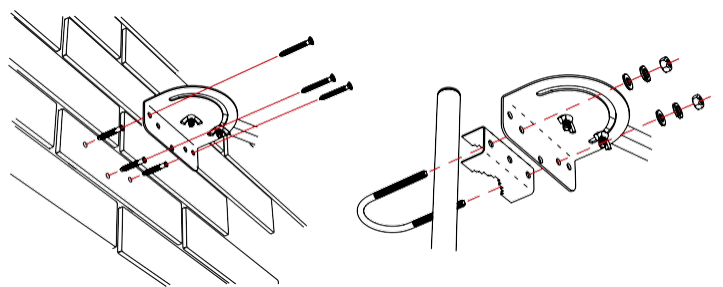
Монтаж установочного кронштейна на стену или мачту
